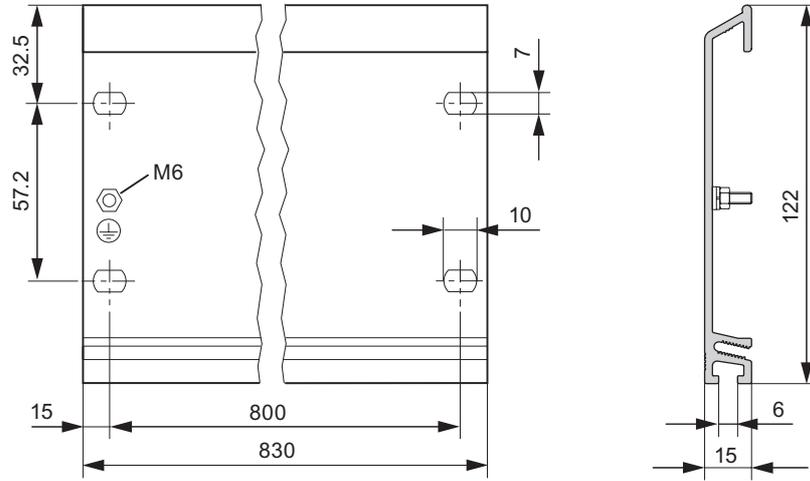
标准宽度为 830 mm 的固定导轨的尺寸图。
